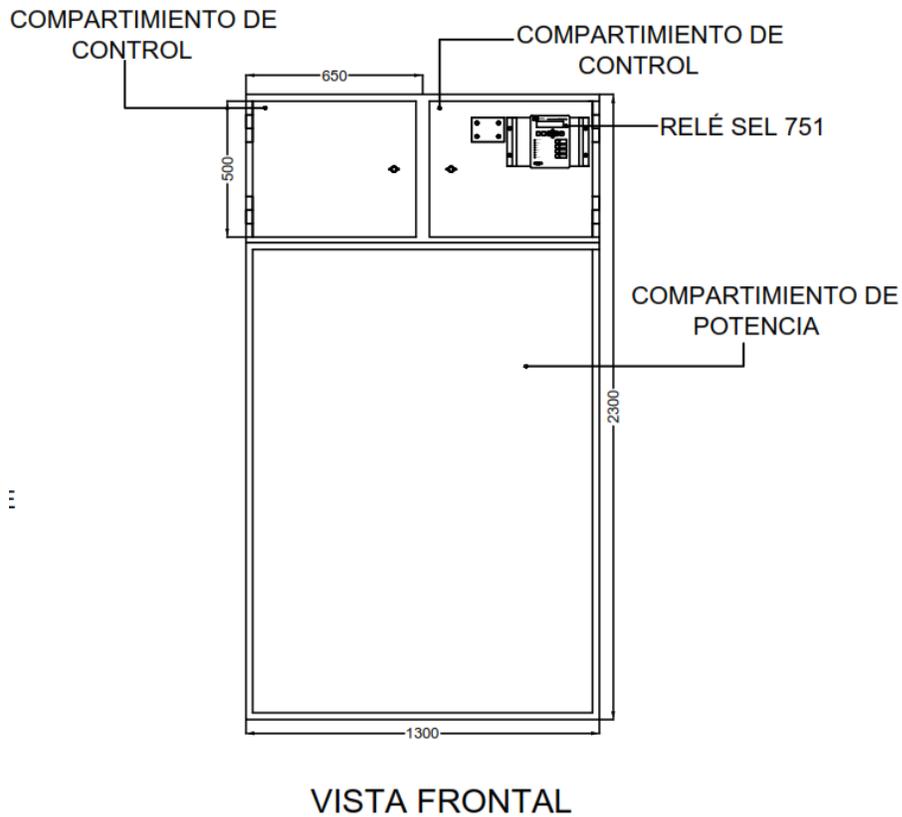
Plano mecánico de celda de conexión – vista frontal externa.
